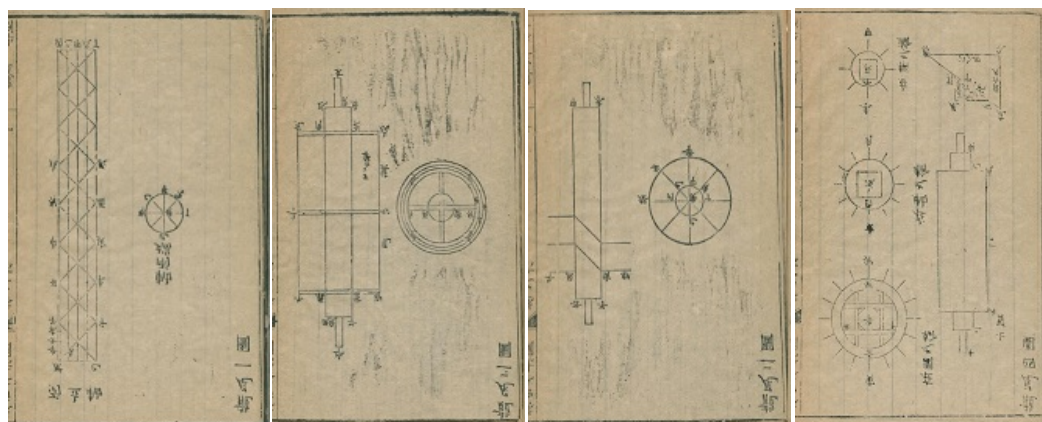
Planos detallados para la construcción del tornillo de Arquímedes
